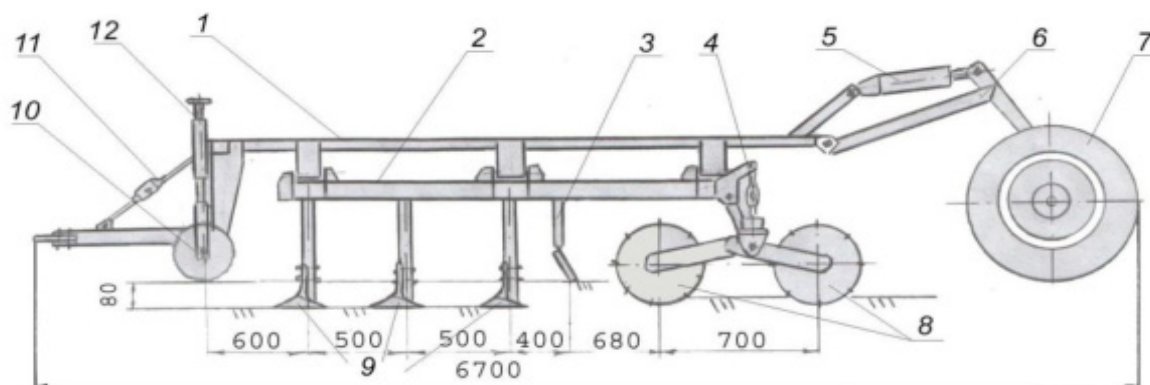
Опытный комбинированный почвообрабатывающий агрегат:
